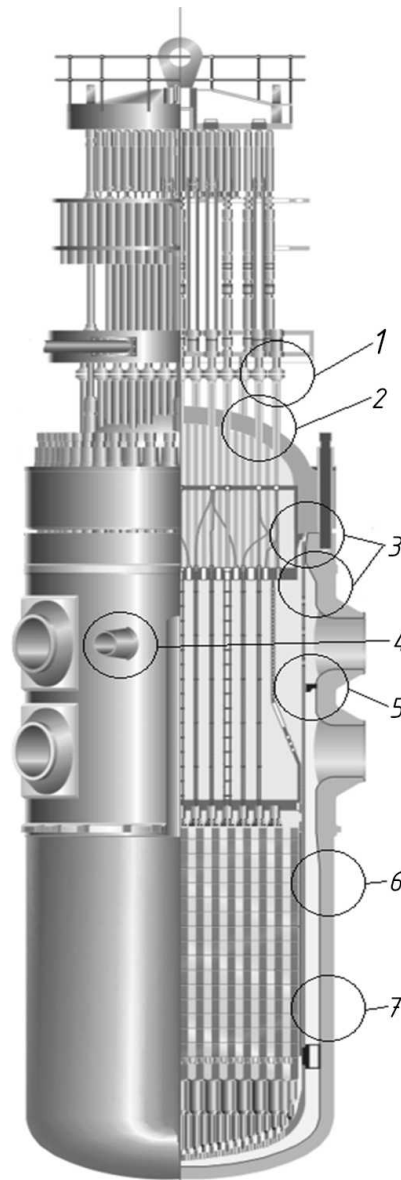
Критичні зони КР: 1 – фланцеві з'єднання СУЗ, КНВ та ТК; 2 – кришка з патрубками СУЗ, КНВ та ТК; 3 – вузол ущільнення реактора; 4 – зона приварювання сорочки патрубка САОЗ до наплавлення реактора; 5 – розділове кільце; 6 – зварне з'єднання № 4; 7 – зварне з'єднання № 3
